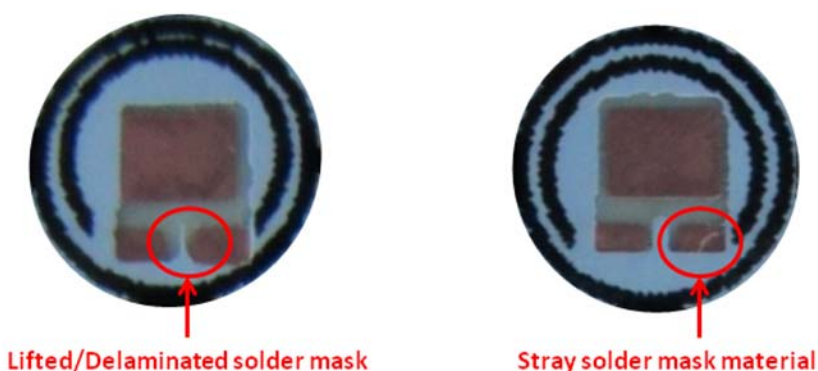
此案例有关劣质的PCB，它可能对PCB和LUXEON发光二极管之间的焊点产生负面影响。
